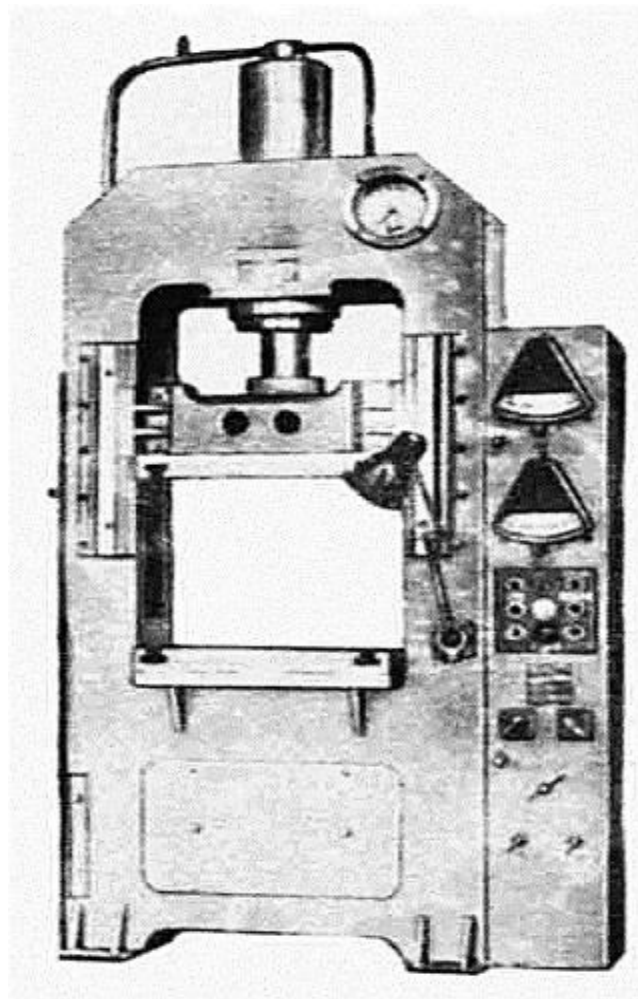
Загальний вид гідравлічного пресу П481А
